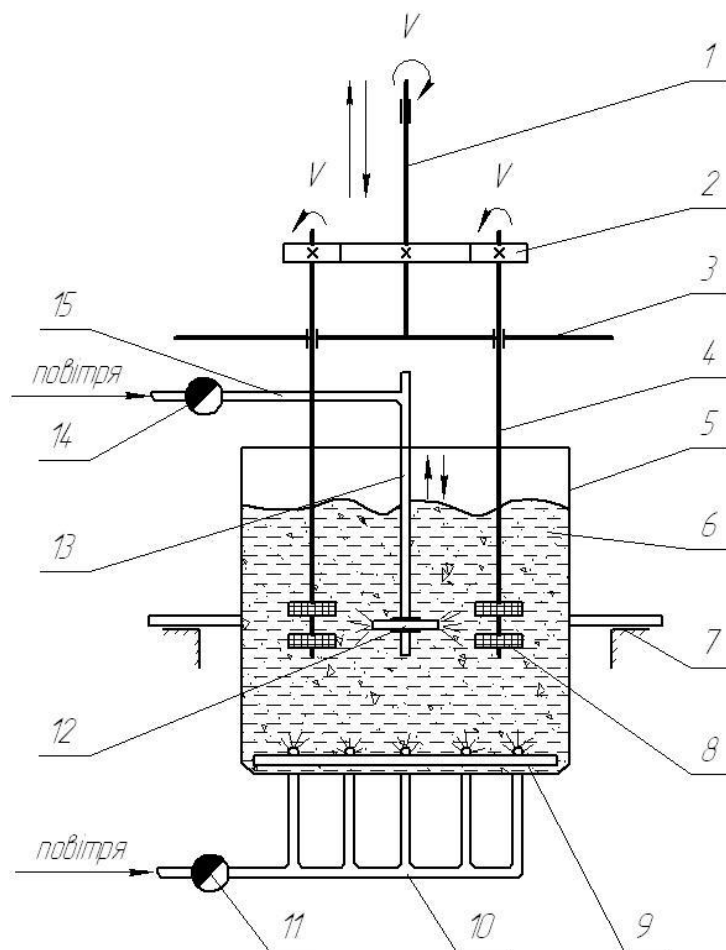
Принципиальная схема устройства для реализации нового способа гидроабразивной обработки затопленными струями. 1 – шпиндельное устройство; 2 – зубчатая передача; 3 – многоместное приспособление; 4 – установочные пальцы; 5 – резервуар; 6 – рабочая среда; 7 – жесткая опора; 8 – обрабатываемы детали; 9 – барботажная система; 10,15 – гибкие трубопроводы; 11,14 – дроссели; 12 – эжекционное сопло струйного аппарата; 13 – штанга
